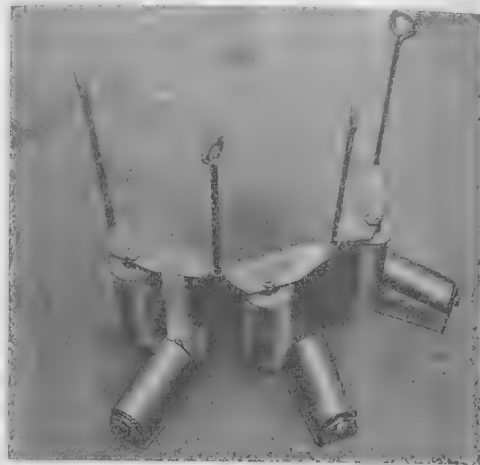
Drei zusammengebaute Eckrollen mit Stahlrollen.
